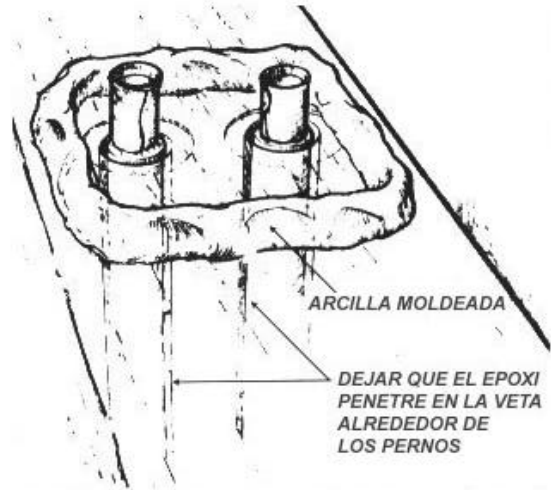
Construya un hueco para epoxi alrededor de cada perno de la quilla.
